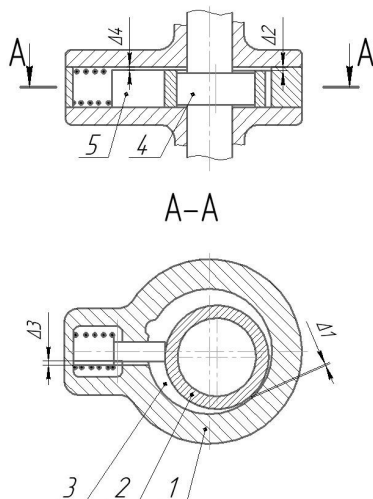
Схема конструкции герметичного ротационного компрессора и схема зазоров в его рабочей камере:
